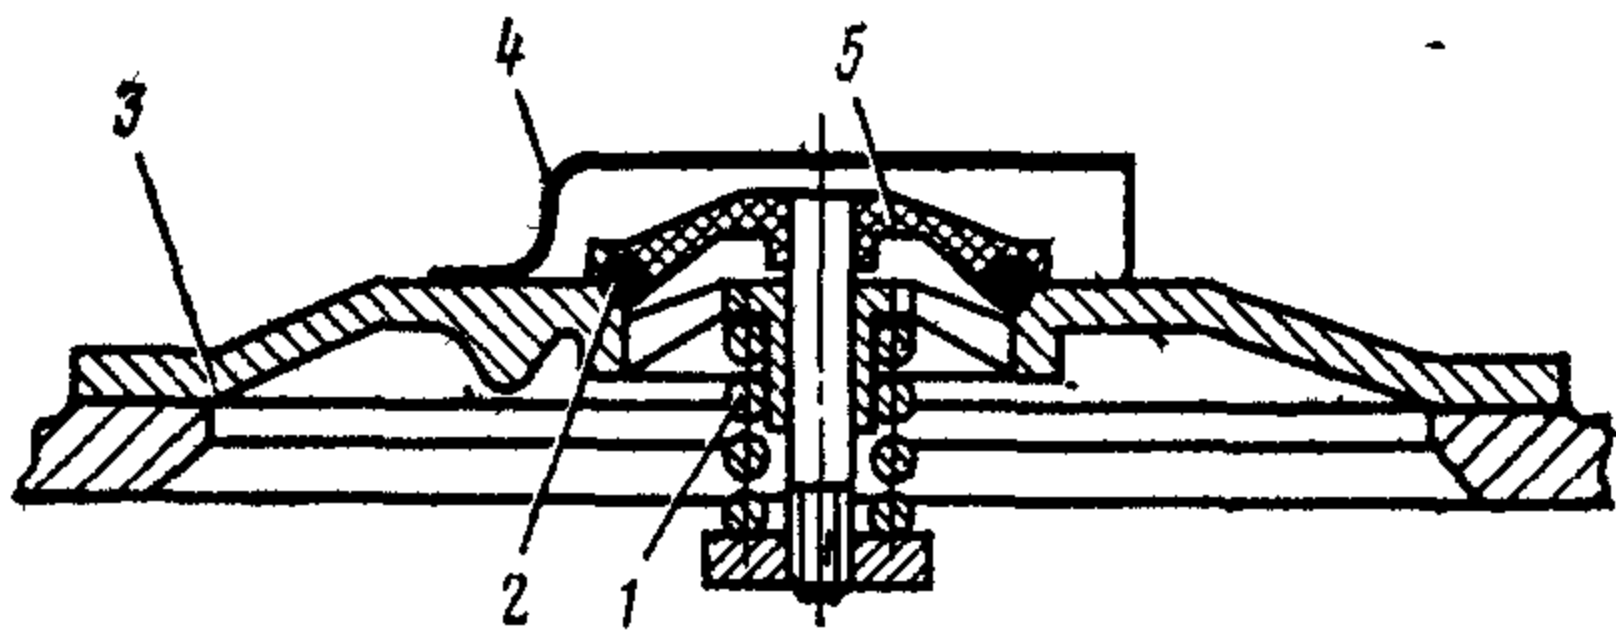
Схема предохранительного клапана двигателя ЧСП18/22
